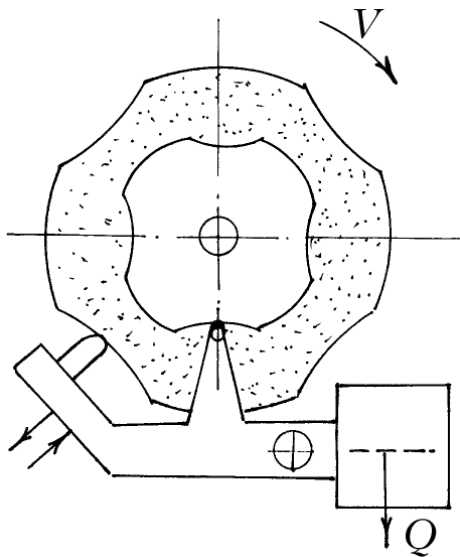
Схема формування регулярного рельєфу на крузі за рахунок змушених механічних коливань.
